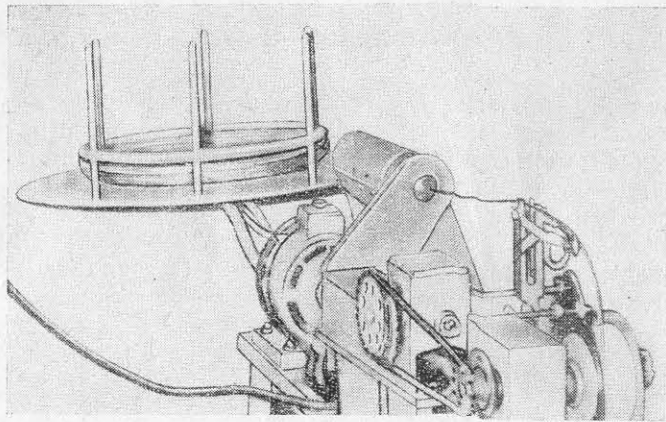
Станок для намотки сварочной проволоки в кассеты для полуавтоматической сварки.
